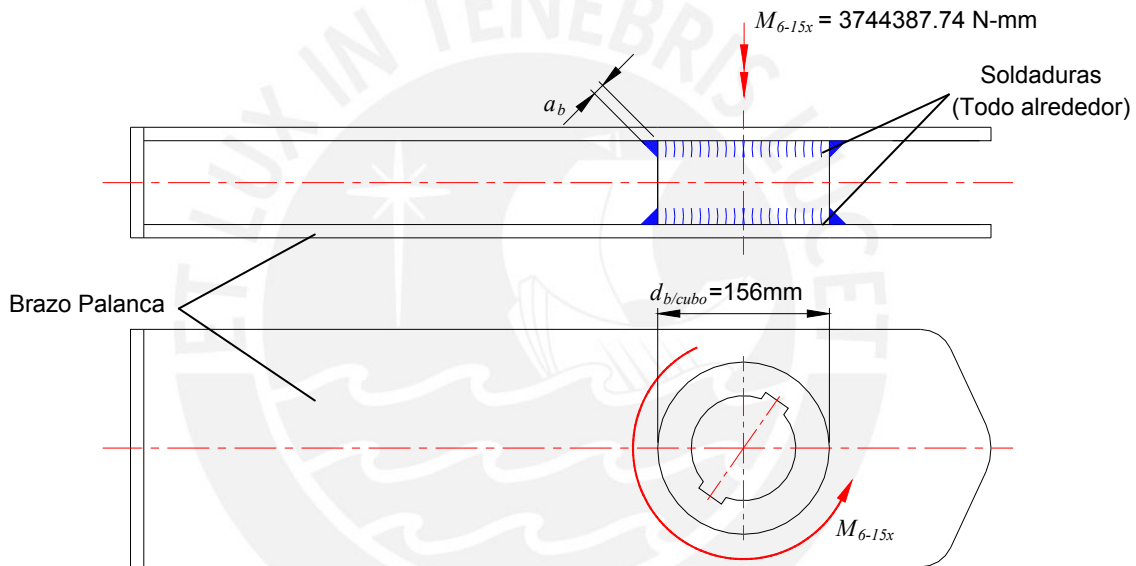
Disposición de las soldaduras del cubo del brazo palanca [Elaboración propia]
